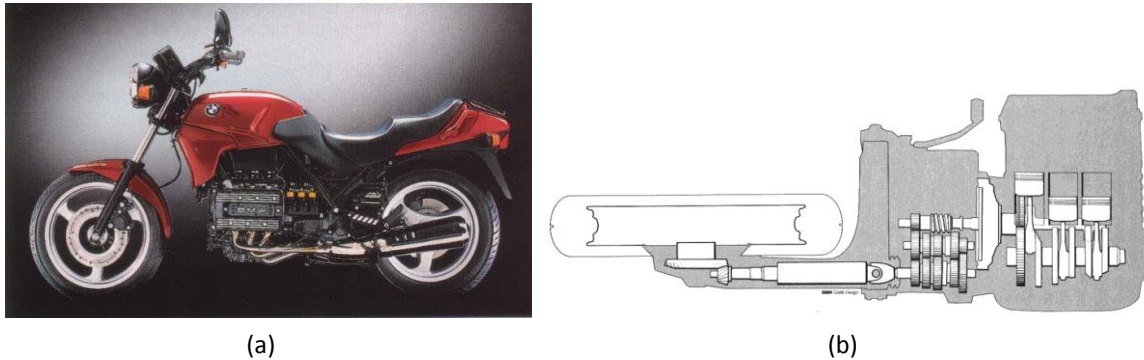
Origem do motor de combustão adaptado: (a) Motociclo *BMW K75*; (b) Detalhe do motor incorporado no motociclo (vista superior).
